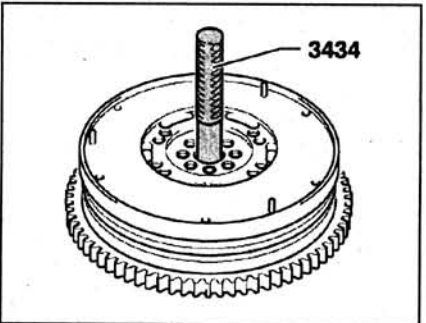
Запрессуйте новый игольчатый подшипник с помощью оправки 3434.
